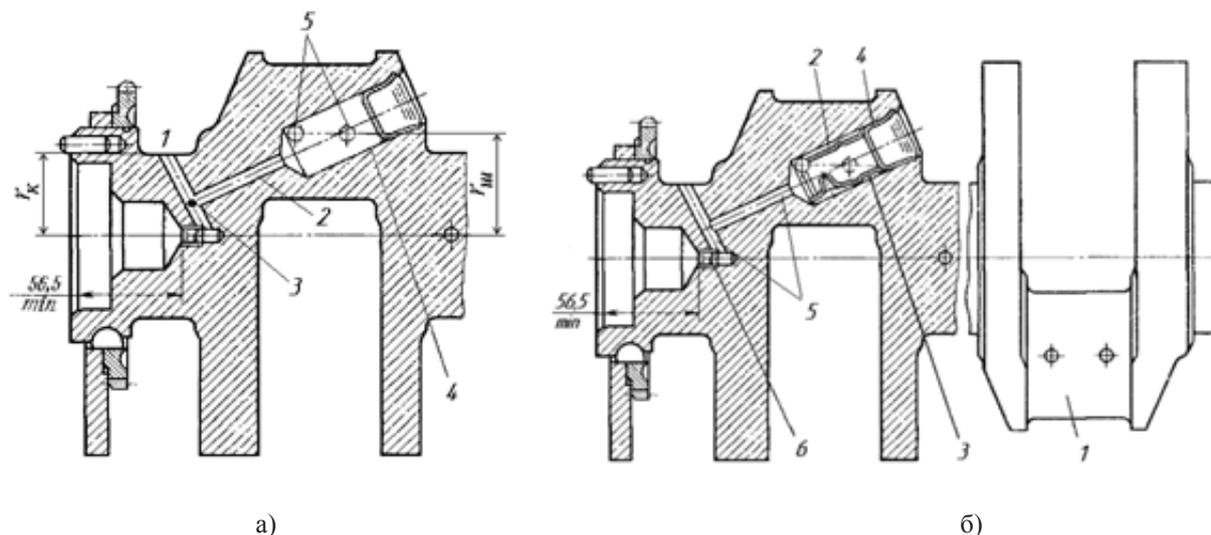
Схемы подвода масла к шатунным подшипникам коленчатого вала двигателя КамАЗ-740.10:
